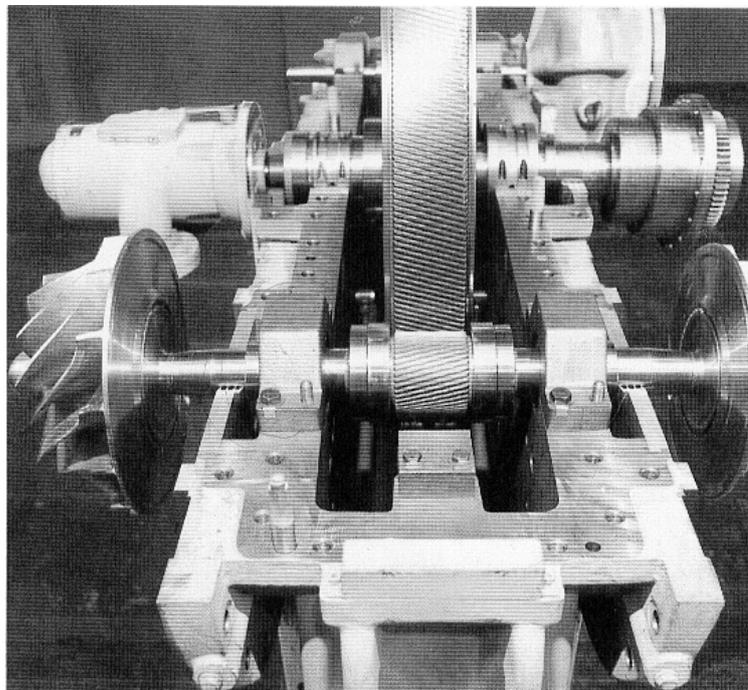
б. Вид на быстроходный и тихоходный роторы многовального центробежного компрессора (корпуса ступеней и верхняя крышка корпуса повышающей зубчатой передачи сняты)
